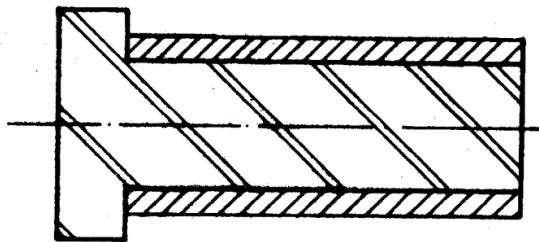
Sobremetal bilateral removido em rebaixos de superfícies cilíndricas
